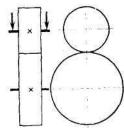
Схема фрикционной цилиндрической передачи с внешним зацеплением
